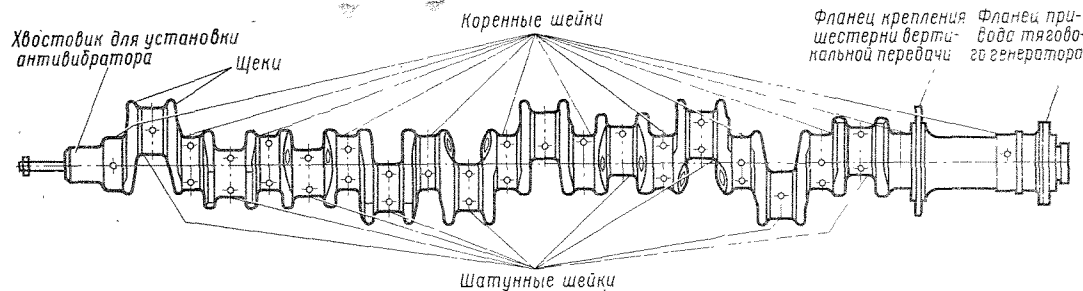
Нижний коленчатый вал дизелей 10Д100, 2Д100
